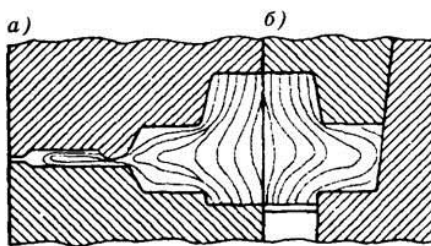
Схема расположения волокон металла при открытой (а) и закрытой (б) штамповке
